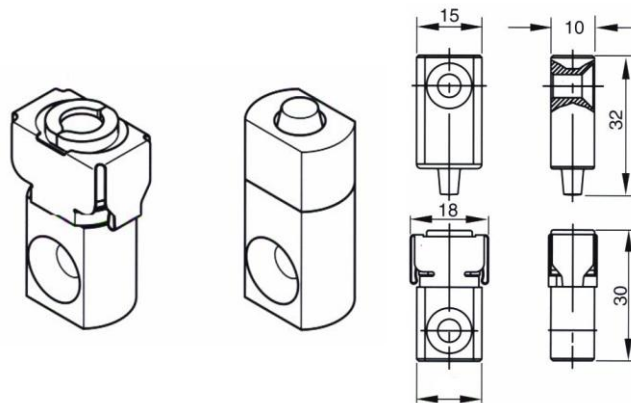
Beispiel des runden Druckfüge-Werkzeugs (R-DF)
